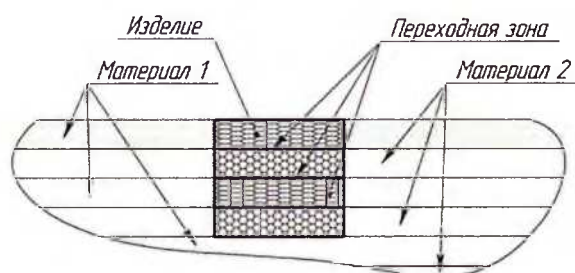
Схема селективного лазерного сплавления порошков двух металлических сплавов
